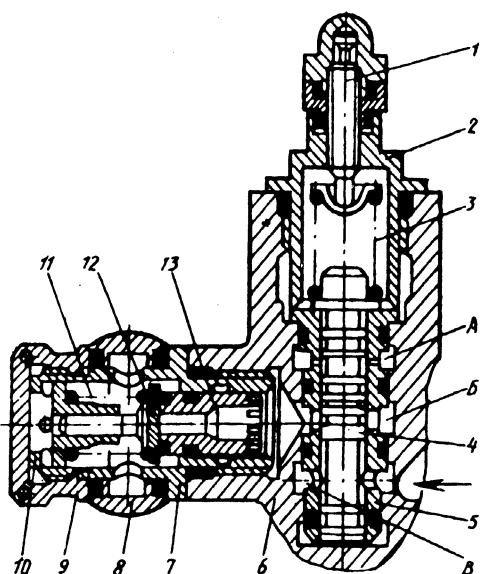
Распределительный и запорный клапаны второго контура форсунок:
